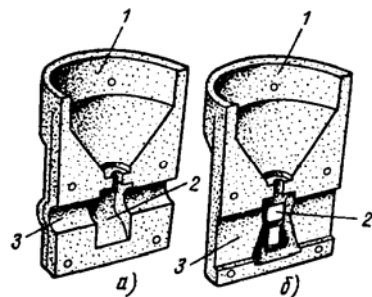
Песчано-смоляные тигель-формы для термитной сварки стальных полос и стержней заземления:
